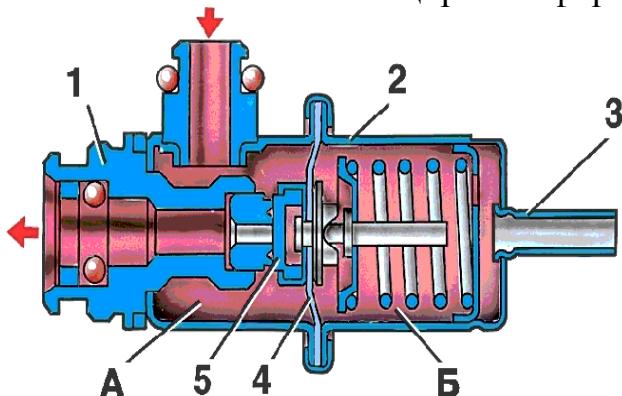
Регулятор тиску палива: 1 - корпус; 2-кришка; 3-патрубок для вакуумного шланга; 4 - діафрагма; 5 - клапан; А - паливна порожнина; Б - вакуумна порожнина.
